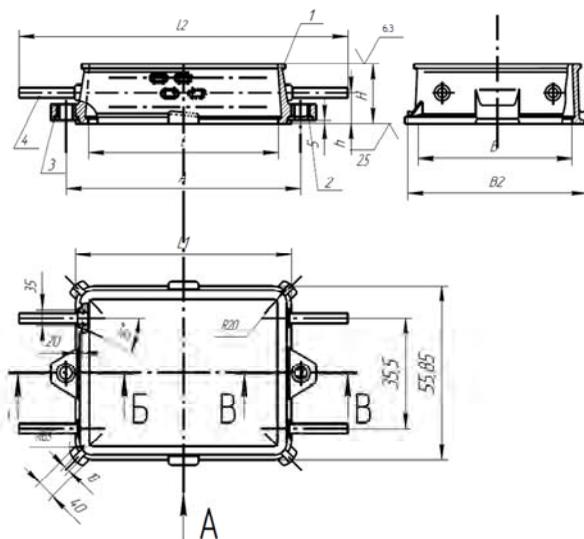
Конструкция цельнолитой чугунной опоки с размерами в свету: длиной 400, 450 и 500 мм, шириной 300, 350 и 400 мм, высотой от 100, 125, 150 и 200 мм 1 – корпус; 2 – втулка направляющая; 3 – втулка центрирующая; 4 – ручки
